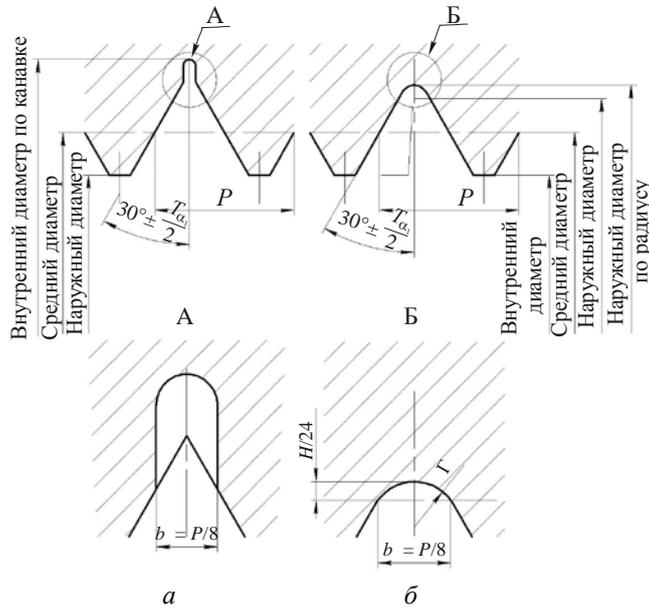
Полный профиль резьбы калибров-колец для метрической резьбы:
